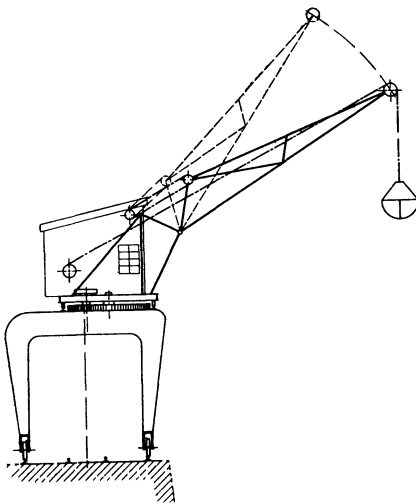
Drehkran mit einziehbarem Ausleger auf Portalgerüst. Stuckenholz.
